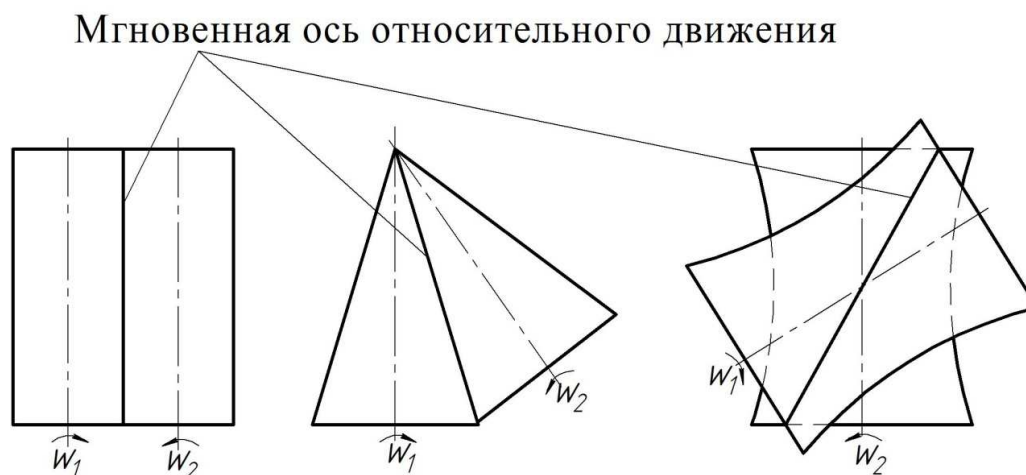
Аксоидная поверхность зубчатого колеса передачи
